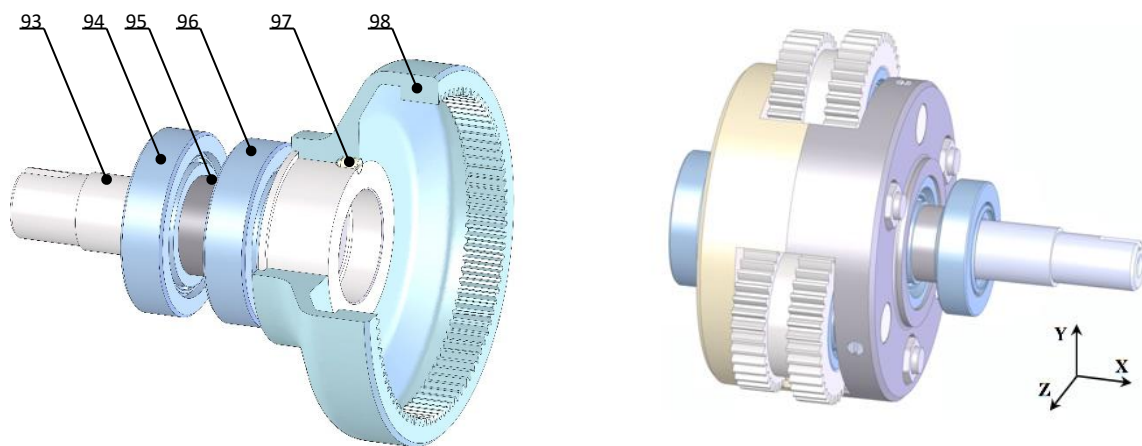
Складальні одиниці виробу «Редуктор планетарний двоступінчатий»: а - вузол вихідного валу; б – вузол вхідного валу
